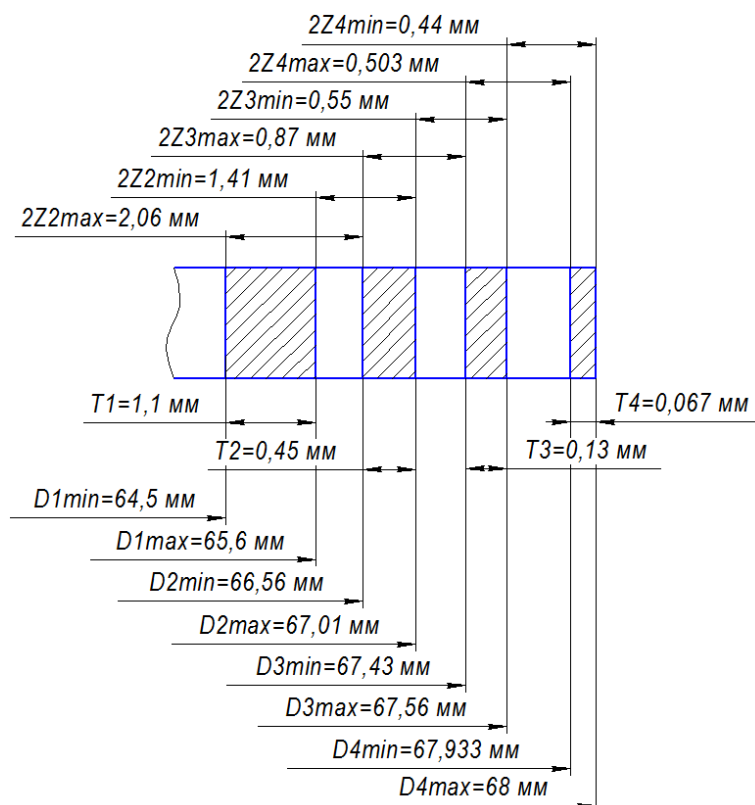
Схема припусков, допусков и промежуточных размеров
